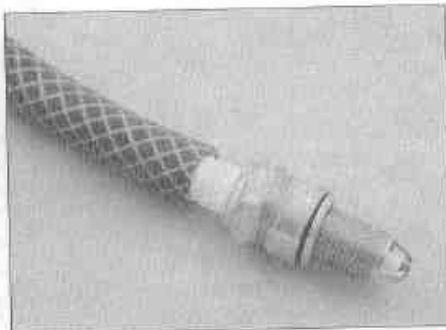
,б. Кусок резинового шланга позволит предотвратить повреждение резьбы при установке свечей зажигания
